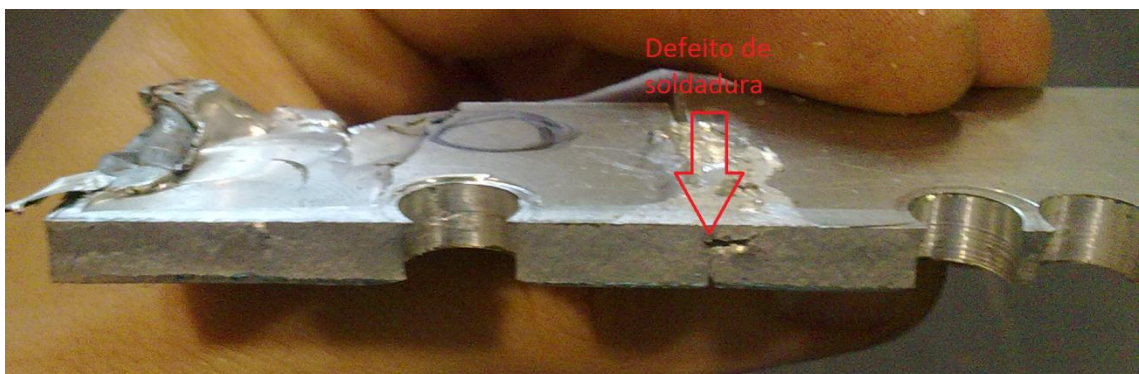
Defeito quando a base da ferramenta FSW não entra em contacto com chapa – secção 1
